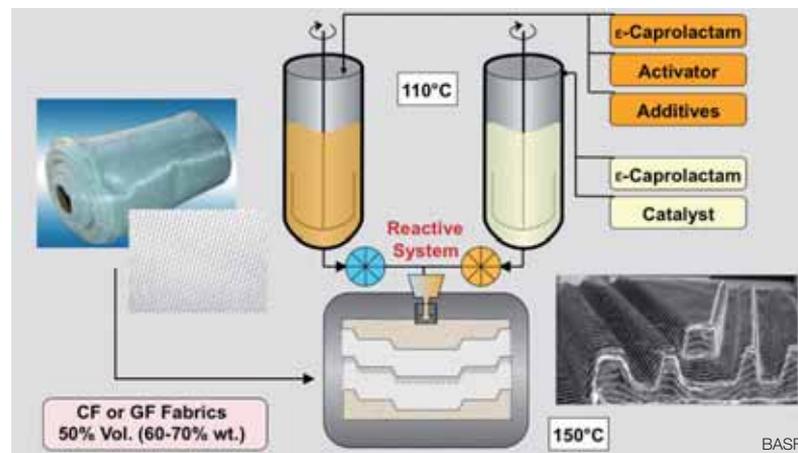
Sequenza del processo RTM (Resin Transfer Molding) per la poliammide
